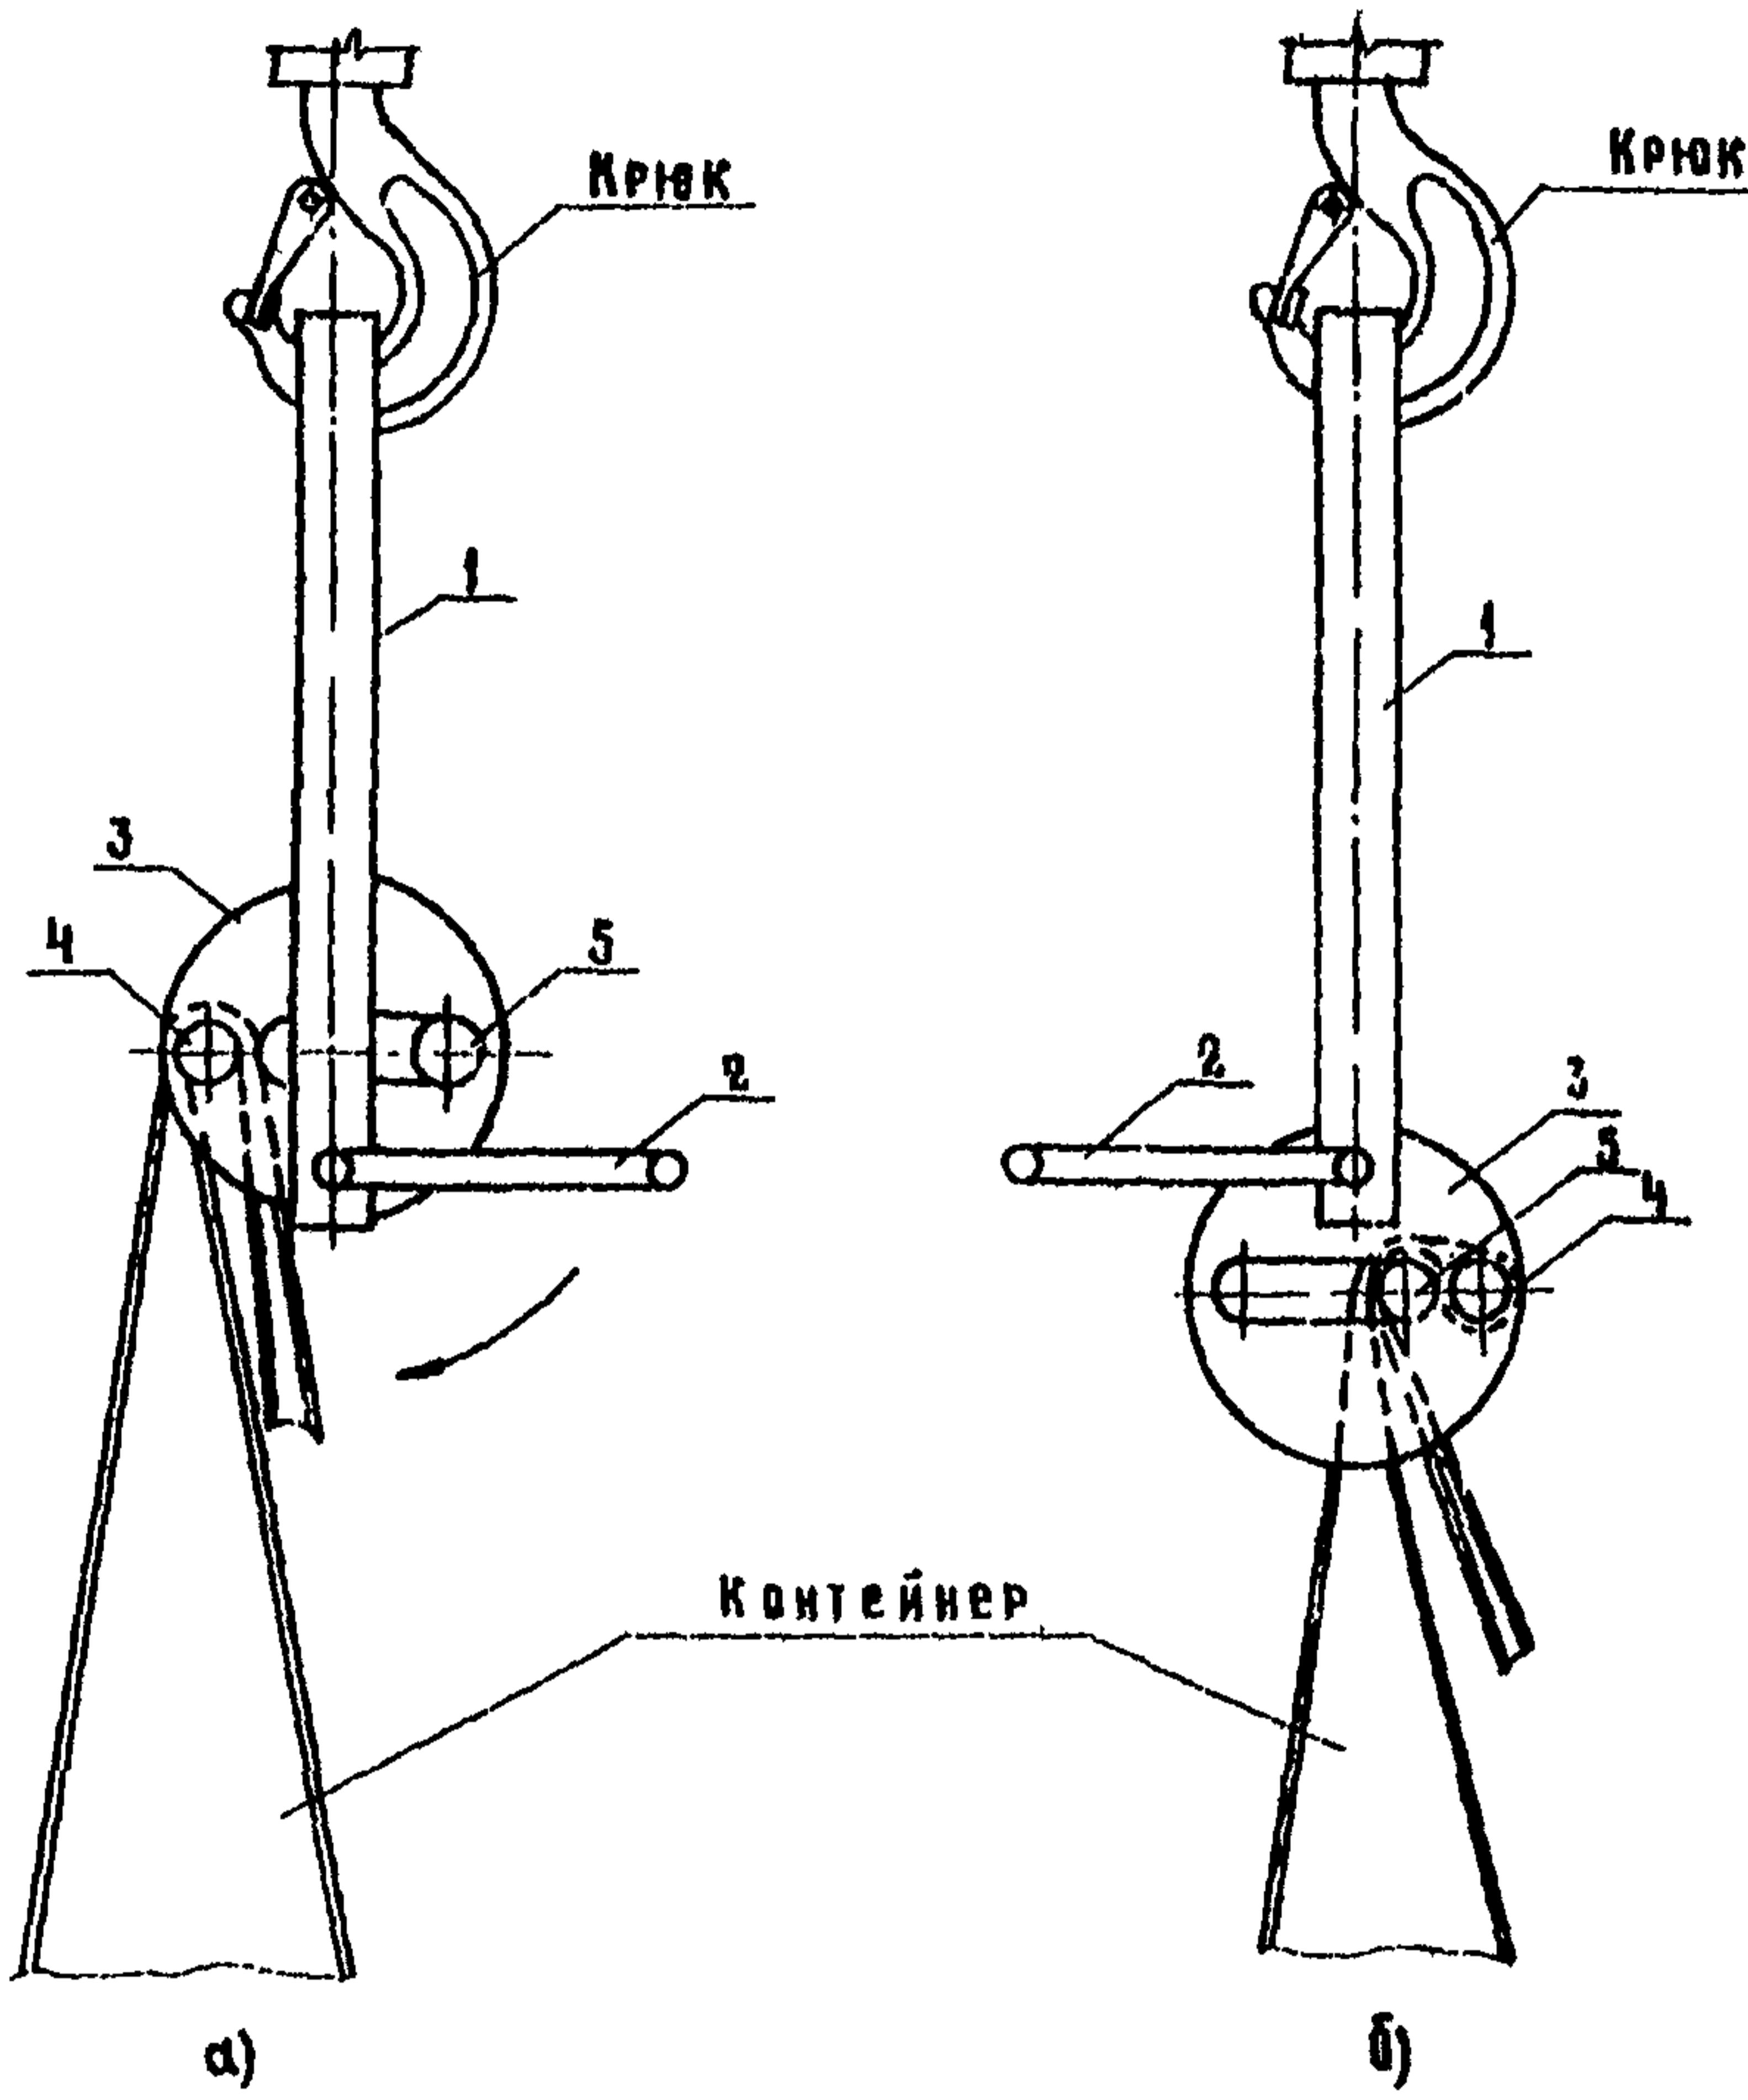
Поршок строповки контейнера грузозахватным приспособлением с полумеханической запаской горловины: 1 - бугель; 2 - рукоятка; 3 - диск; 4- неподвижная штанга; 5 - подвижная штанга
